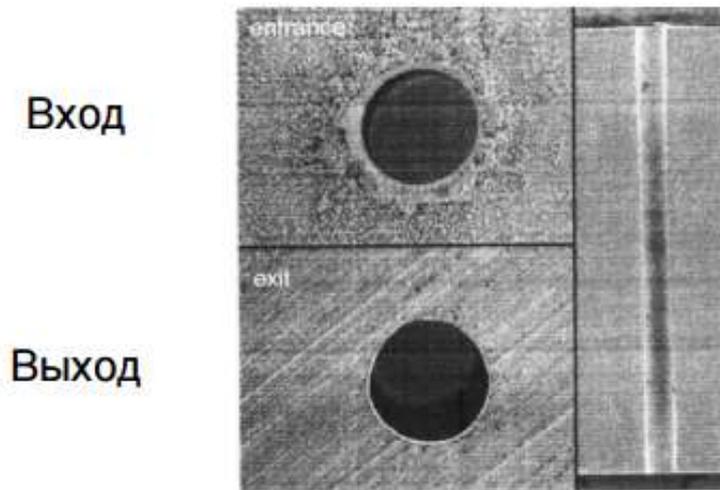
Отверстия в стали, полученные лазерным сверлением
